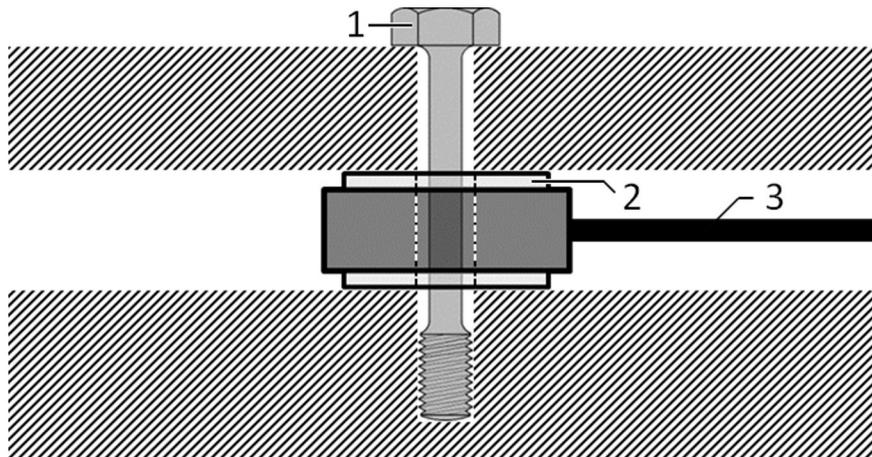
Befestigung des Aktors mit einer Dehnschraube
